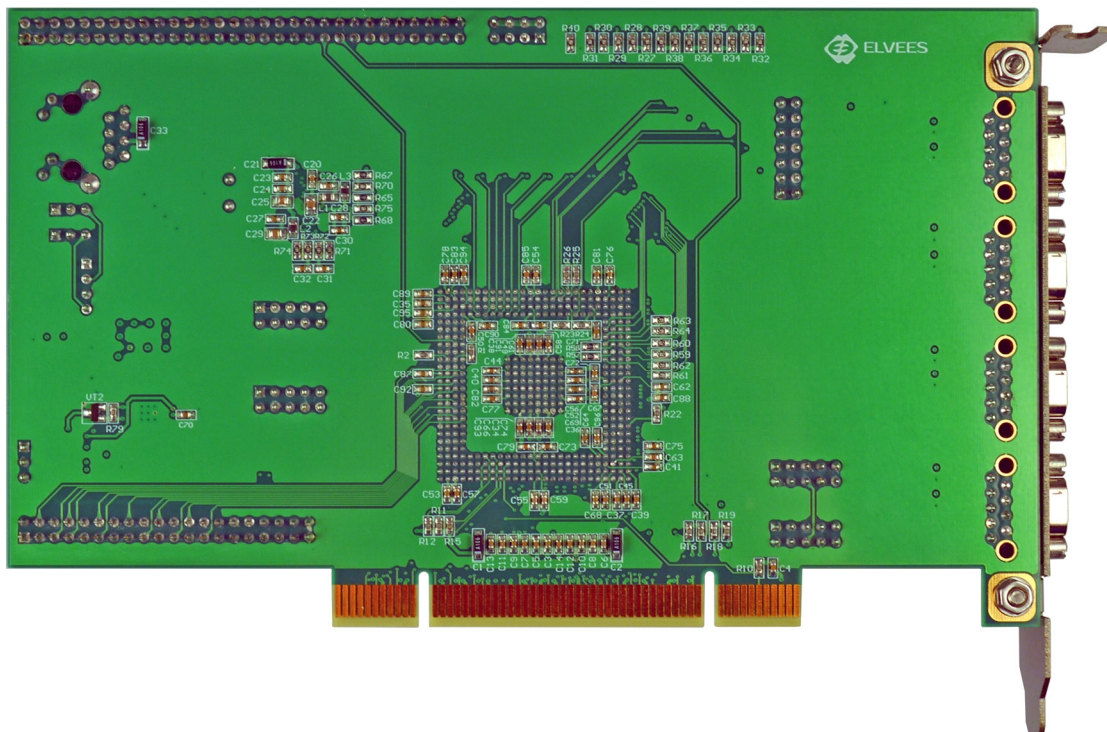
Внешний вид отладочного модуля МСВ-03РЕМ-РСІ. Обратная сторона платы
